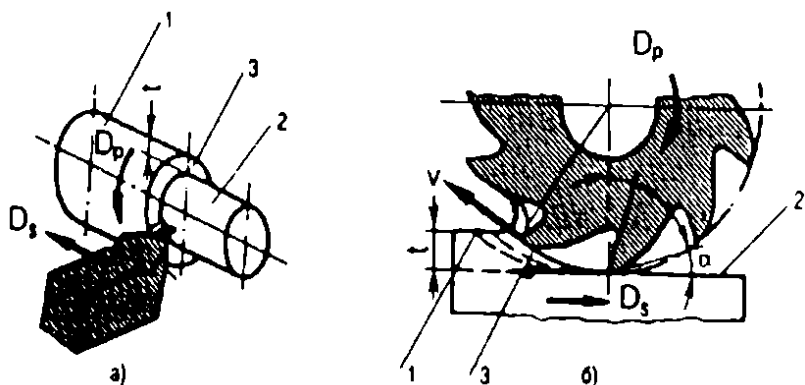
Процессы обработки резанием: а – точение; б – фрезерование:
